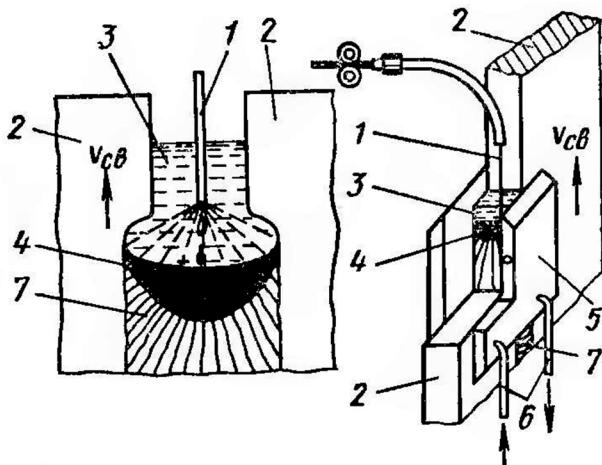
Схема процесса электрошлаковой сварки
